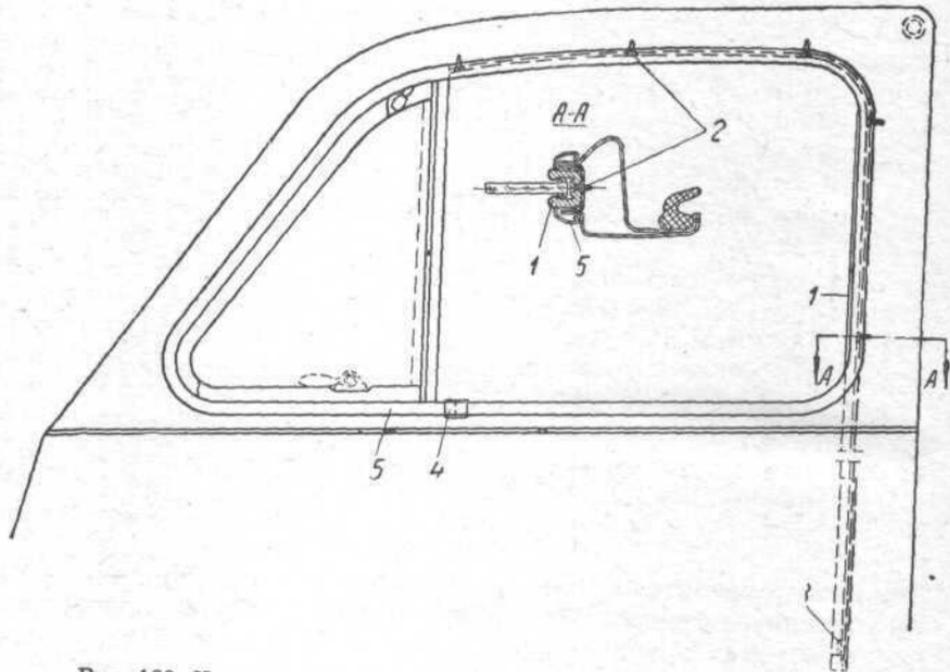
Крепление желобка опускаемого стекла передней двери:
